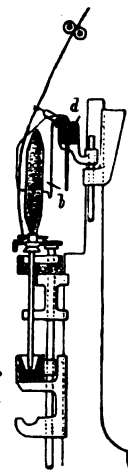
Vorrichtung für Ringspinnmaschinen.
